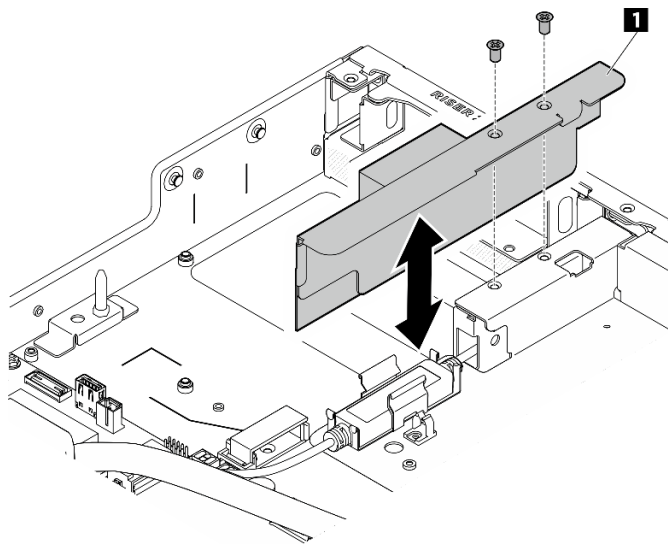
Installieren der DPU-Luftführung und der Halterungsbaugruppe
